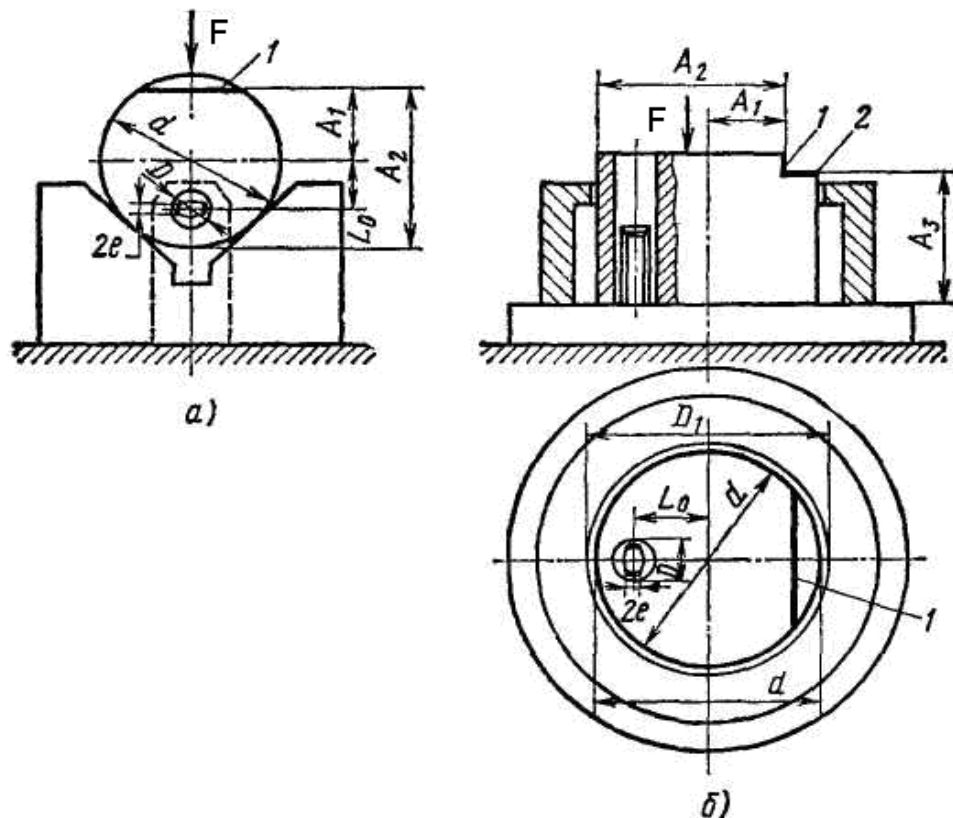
Схема установки заготовки при обробці (до задачі 1.26)
